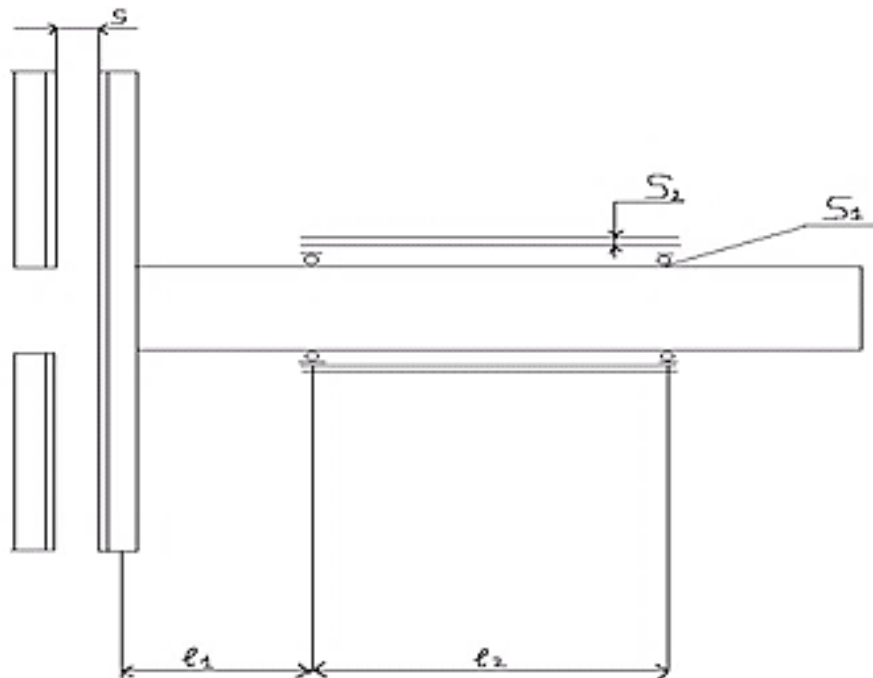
Расчетная схема для расчета биений ротора: S – межножевой зазор; S_1 – радиальный зазор подшипников; S_2 – зазор между стаканом ротора и корпуса
